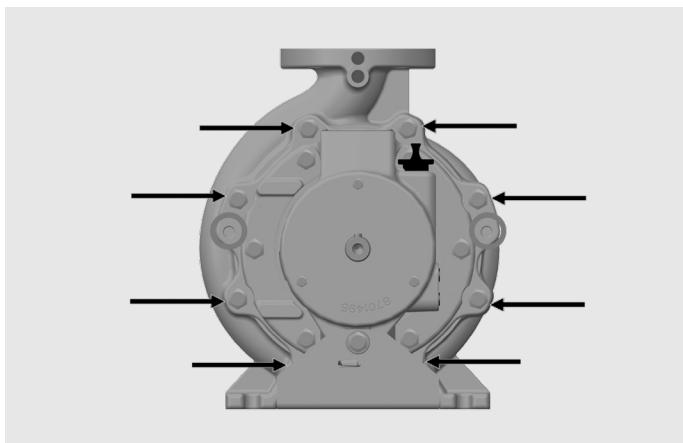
Parafusos entre a tampa de pressão e o caracol
